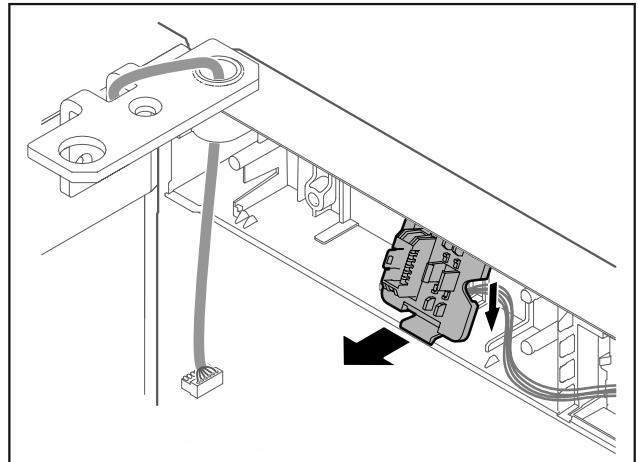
La posición de montaje del soporte del conector puede estar girada 180°.
